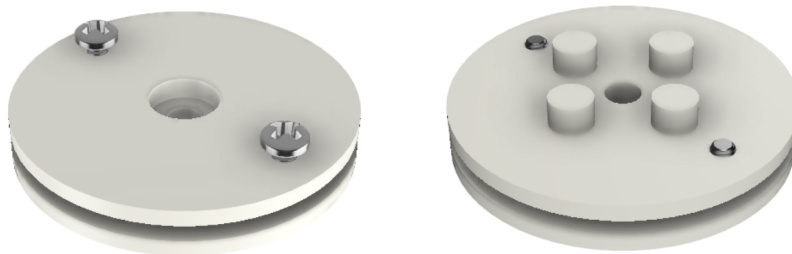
Polea a) parte superior (izquierda), b) parte inferior (derecha).
